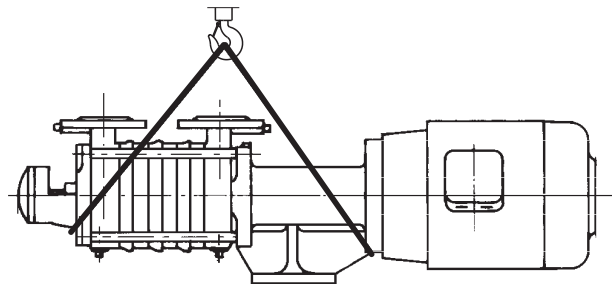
Hebezeug befestigen an Blockpumpe (horizontale Ausführung)
